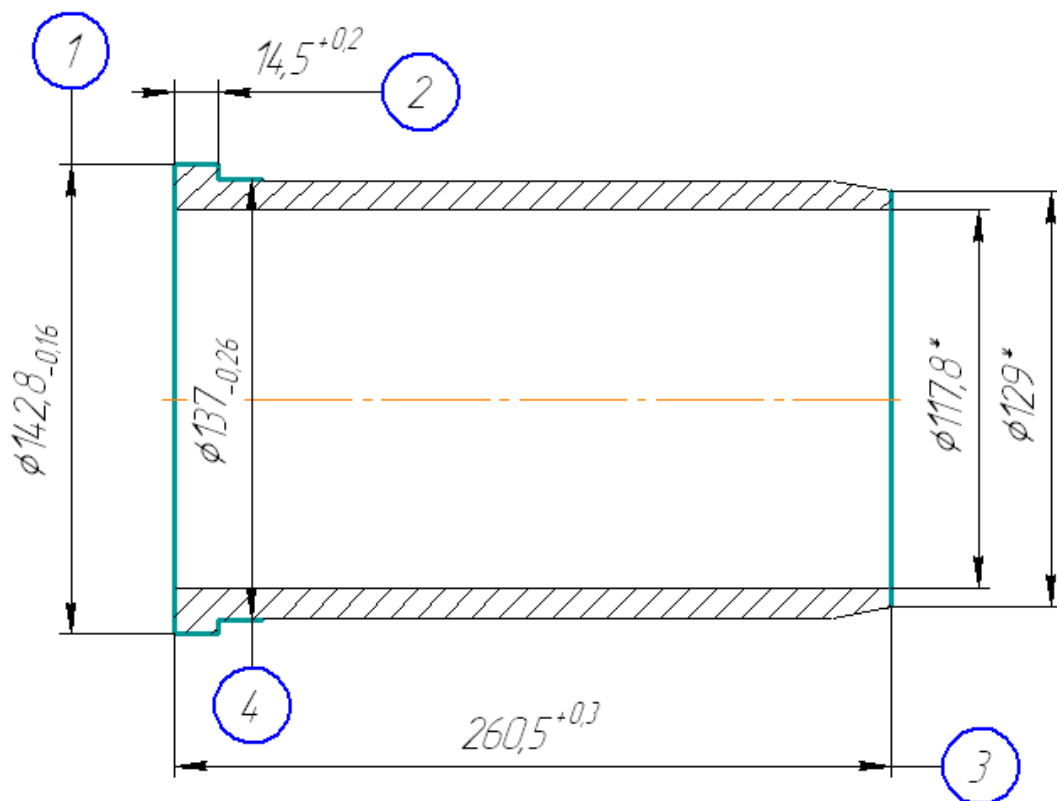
Ескіз обробки заготовки на операції 020
